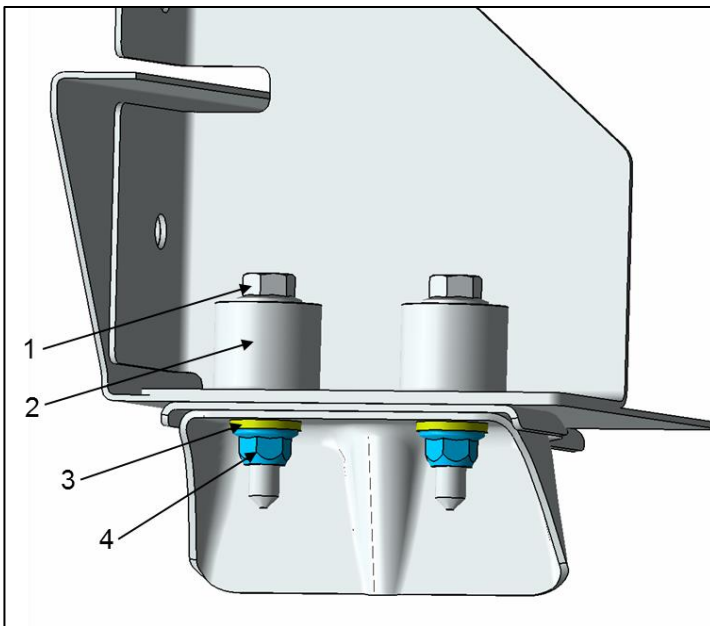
esempio di realizzazione di un collegamento a vite con elemento ammortizzante
